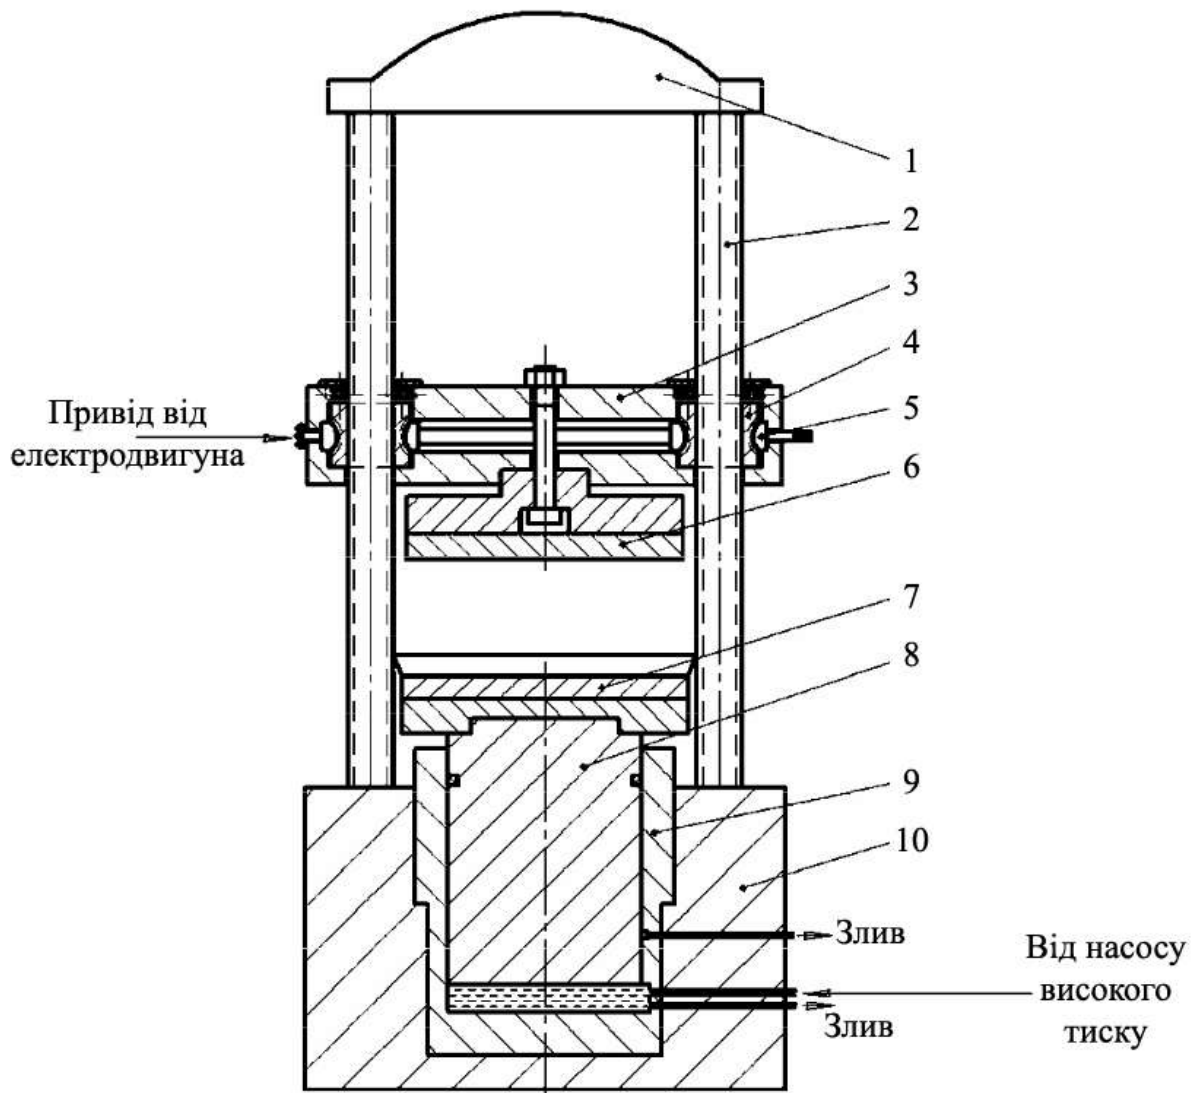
Навантажувальний пристрій пресу П-125: 1 – верхня плита преса; 2 – колони преса; 3 – рухлива траверса; 4 – гайки на колонах; 5 – вал із черв’яками; 6 – верхня плита; 7 – стіл; 8 – плунжер гідроциліндра; 9 – гільза гідроциліндра; 10 – основа преса
